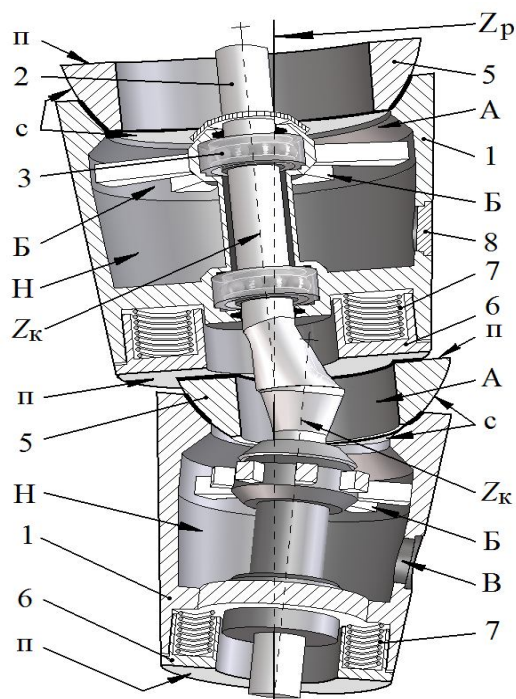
Принцип герметизации раскатывающего рабочего органа, допускающий проникновение грунта внутрь катков: 1 – каток; 2 – вал; 3 – подшипник; 5 – кольцо сферическое; 6 – кольцо прижимное; 7 – элемент упругий; 8 – заглушка  $Z_p$  – геометрическая ось вала раскатывающего рабочего органа;  $Z_k$  – геометрическая ось катка. А – свободное пространство; Б – канал соединительный; В – отверстие ревизионное; Н – полость накопительная.
